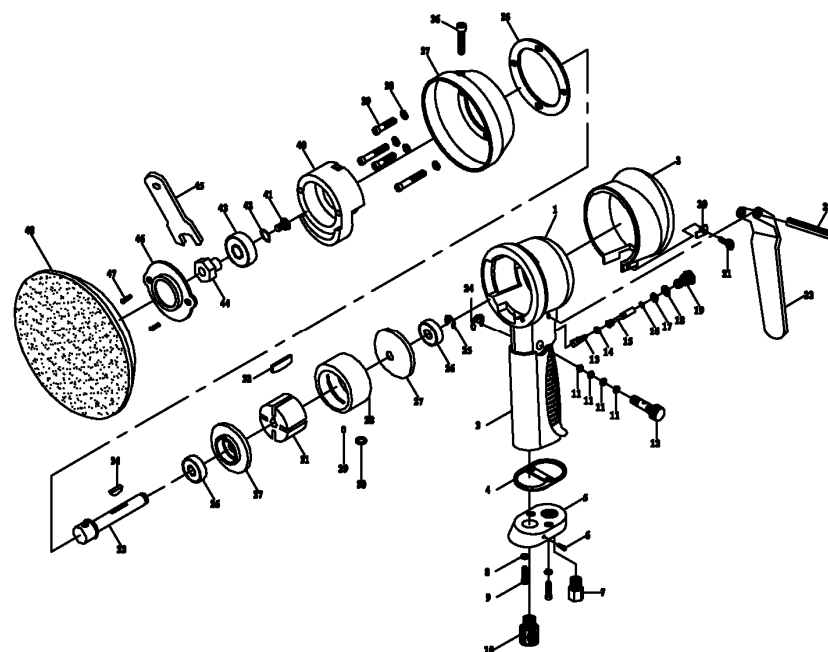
Устройство и схема сборки машины шлифовальной MFG 125/003-2
